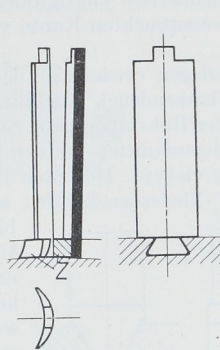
Schaufelbefestigung mittels Schwalbenschwanzes.
